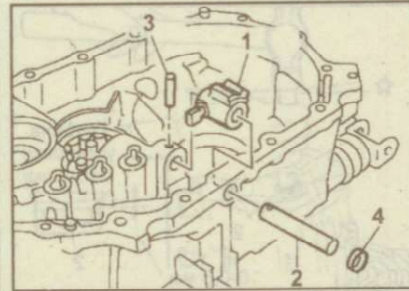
Установка селектора (1), вала селектора (2), штифта (3) крепления вала селектора и заглушки (4)
